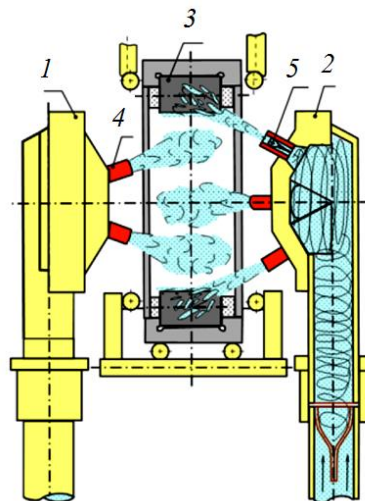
Схема стенду для промивки деталей потоком рідини з кавітаційними пухирцями: 1 ,2 – струменеві-кавітаційні головки; 3 – деталь, що промивається; 4 – сопла; 5 – кавітатор
